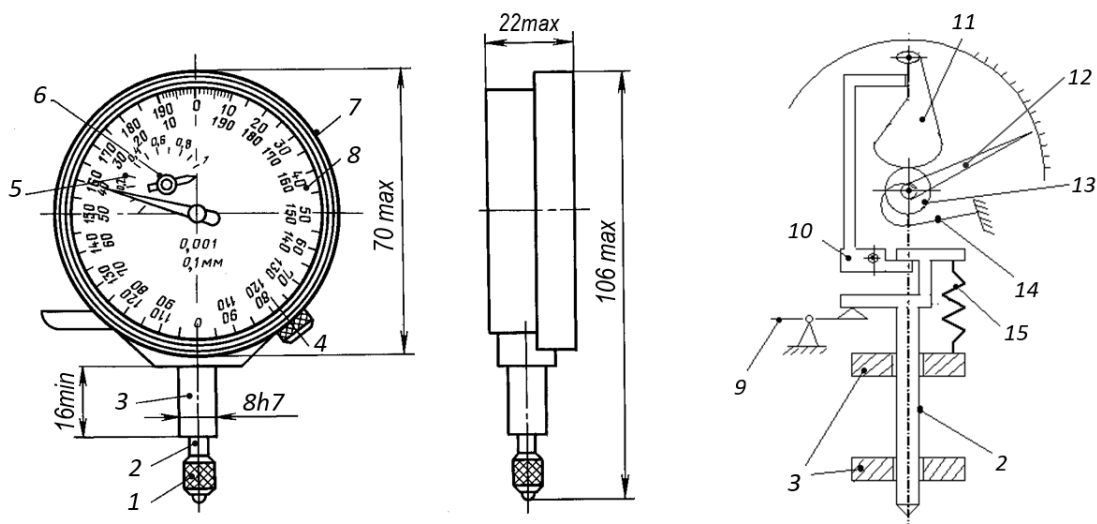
Принципова схема індикатора МИГ-1.
